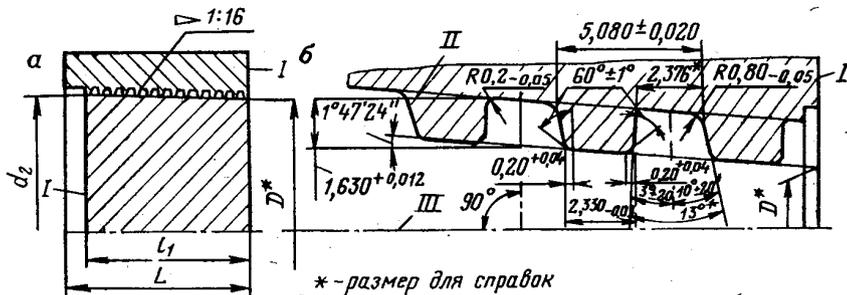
Резьбовой калибр-кольцо Р для контроля резьбы труб ОТТМ; ОТТГ; ТБО:
